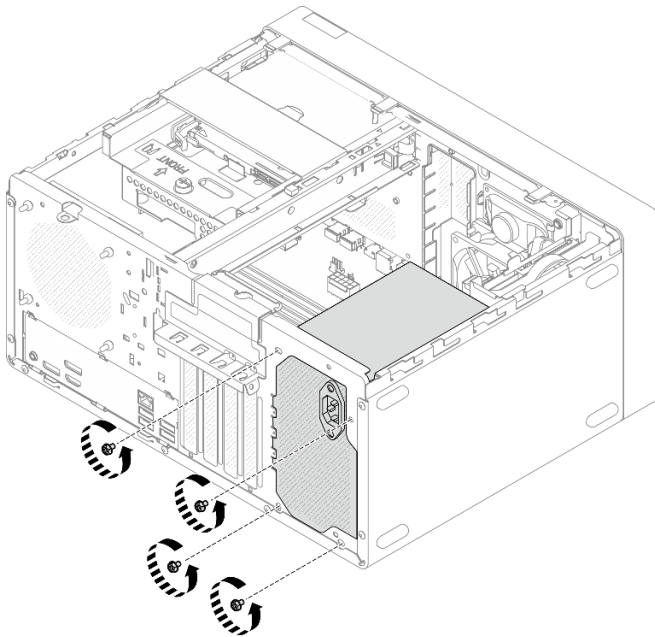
Entfernen der Schrauben, mit denen die Netzteileneinheit befestigt ist
